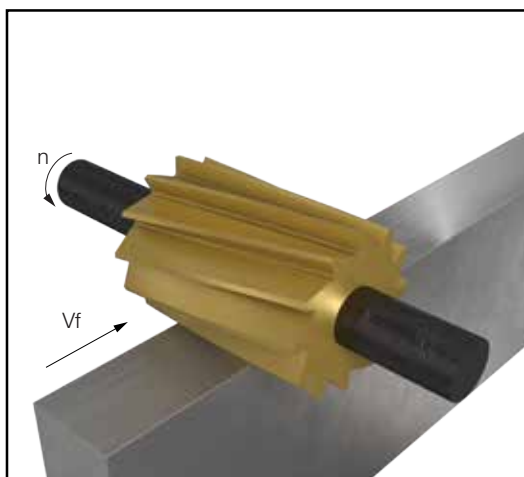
Обработка цилиндрической фрезой и фрезерование высоких уступов
